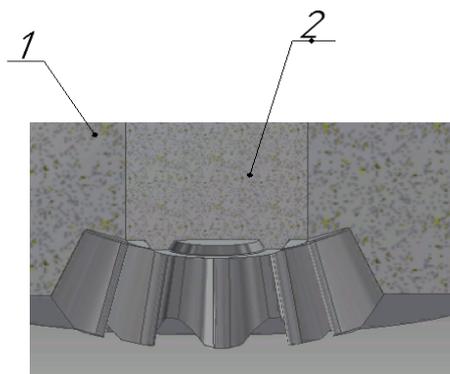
Составная конструкция верхней полуматрицы (1 – полуматрица, 2 – вставка)
